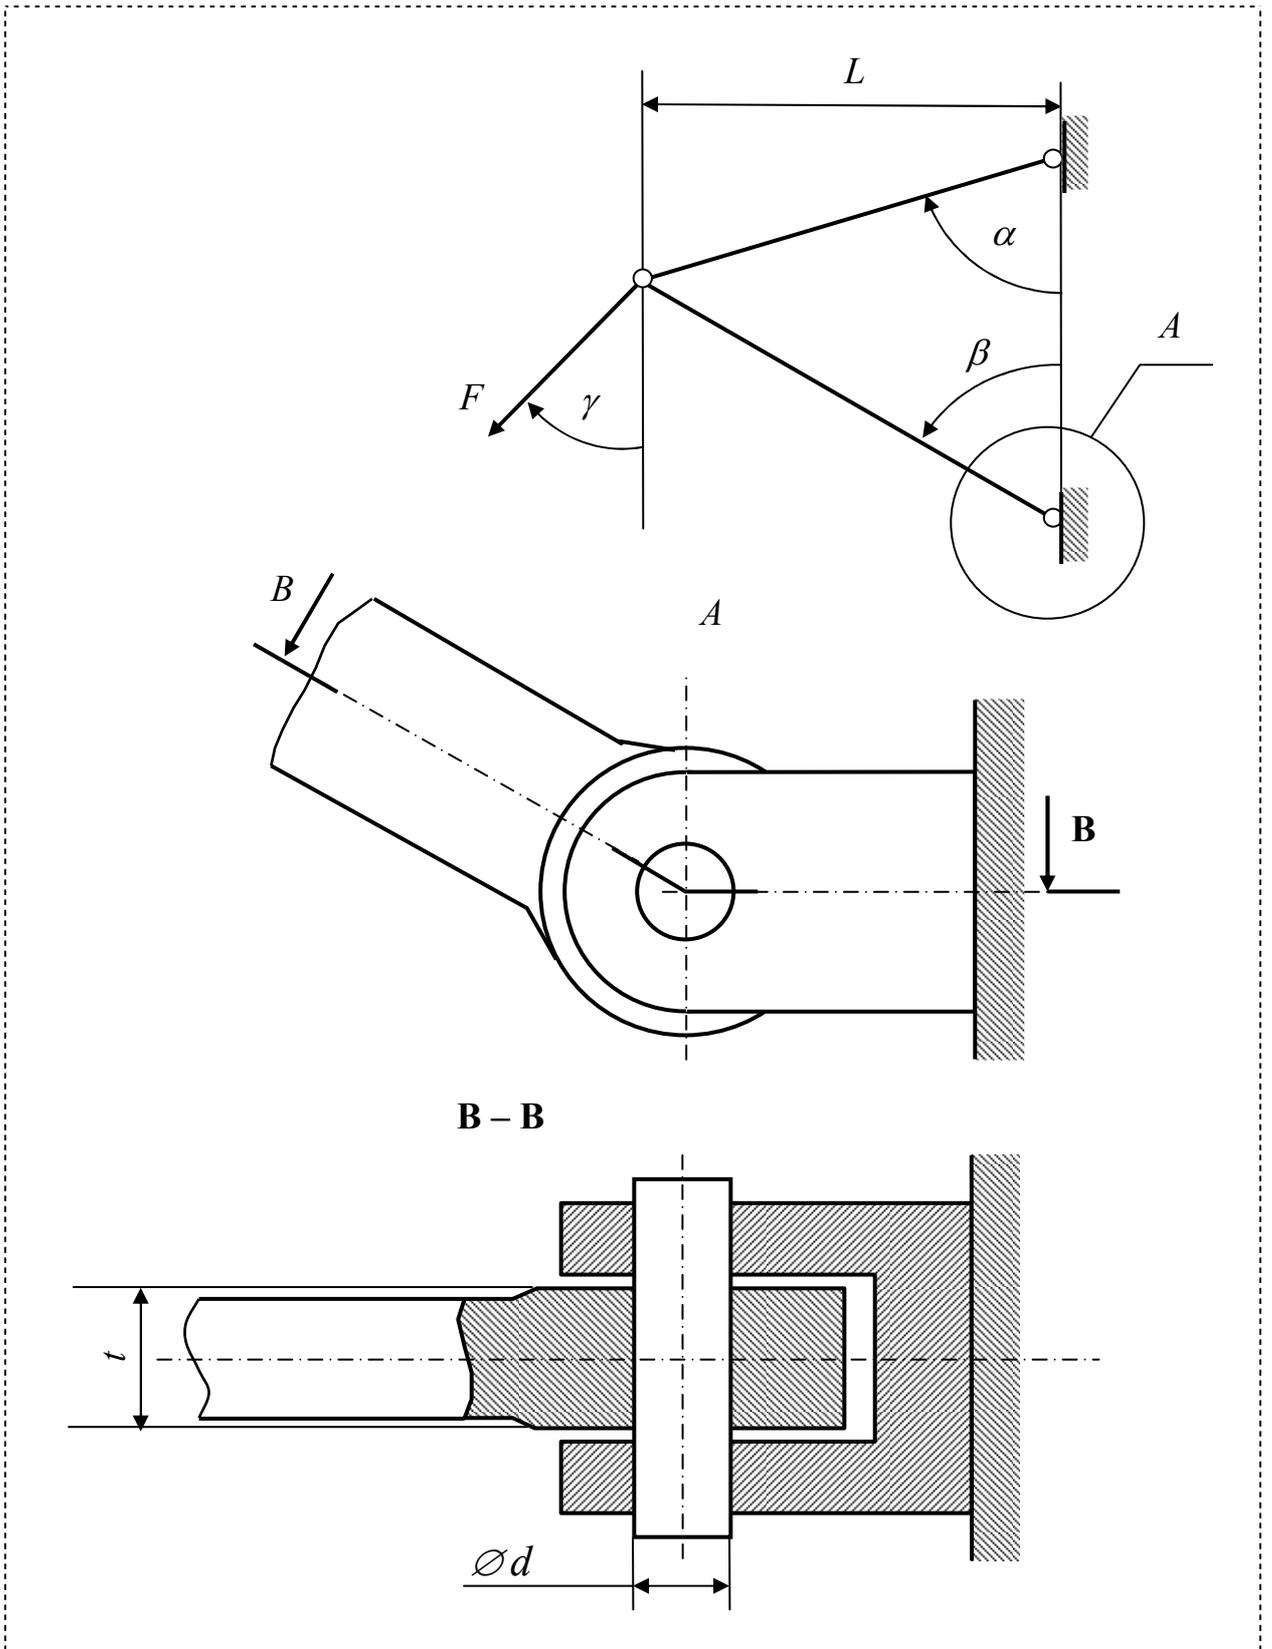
Схема плоской фермы и цилиндрического шарнира
